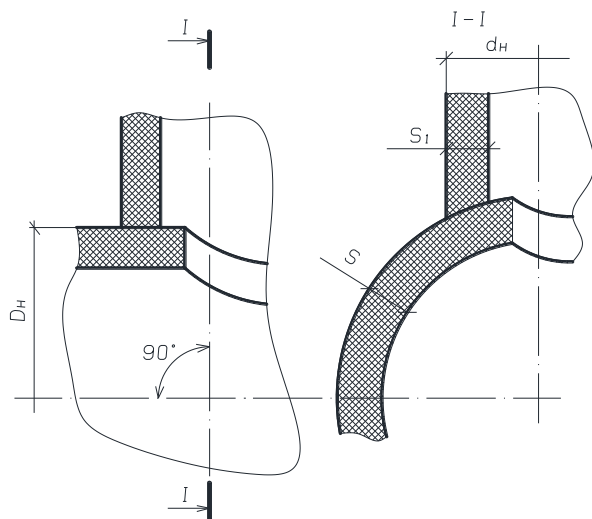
Конструктивные элементы подготовленных кромок (швы ТЗ)
